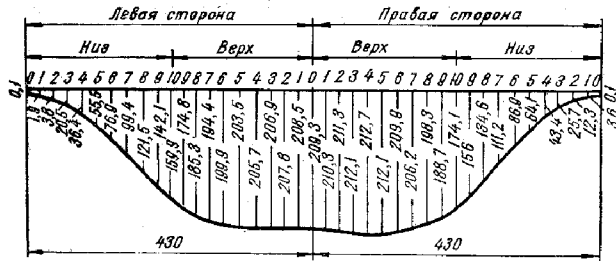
Развертка конца отрезка сварного тройника.
